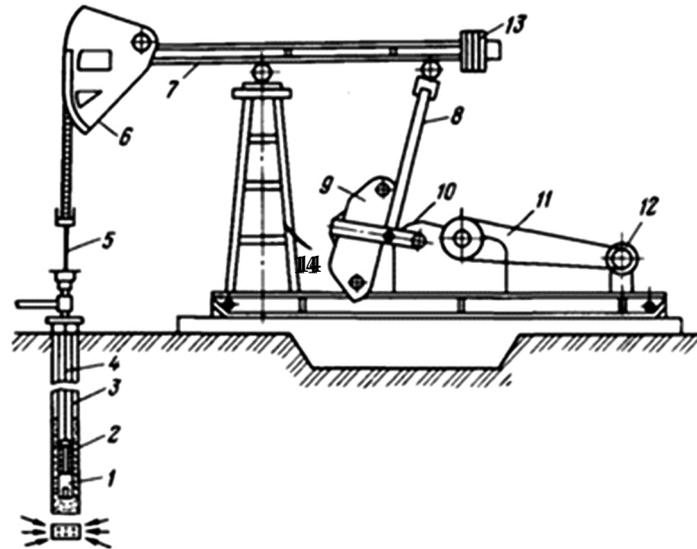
Схема глубинно-насосной установки: 1 – плунжерный глубинный насос; 2 – плунжер; 3 – насосные трубы; 4 – штанга; 5 – полированный шток; 6 – головка балансира; 7 – балансир; 8 – шатун; 9 – кривошипный противовес; 10 – редуктор; 11 – клиноременная передача; 12 – электродвигатель; 13 – балансирный противовес, 14 – стойка
